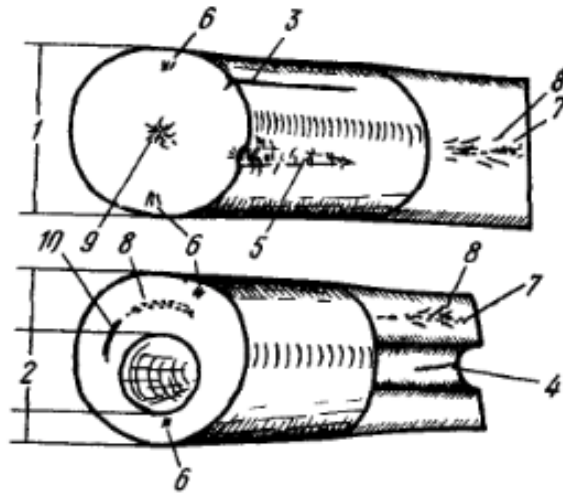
Основные виды дефектов сплошных (а) и полых (б) заготовок цилиндрического сечения.
